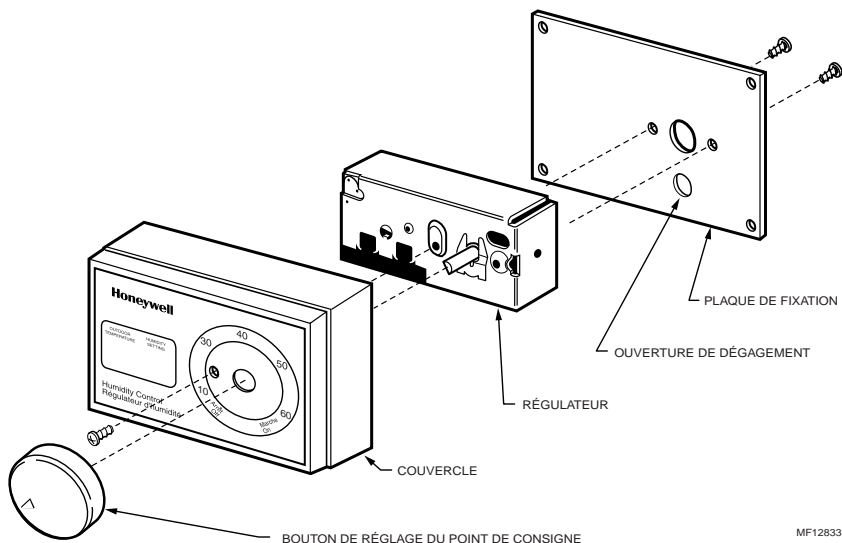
Assembler le régulateur en vue de l'installer au mur.
